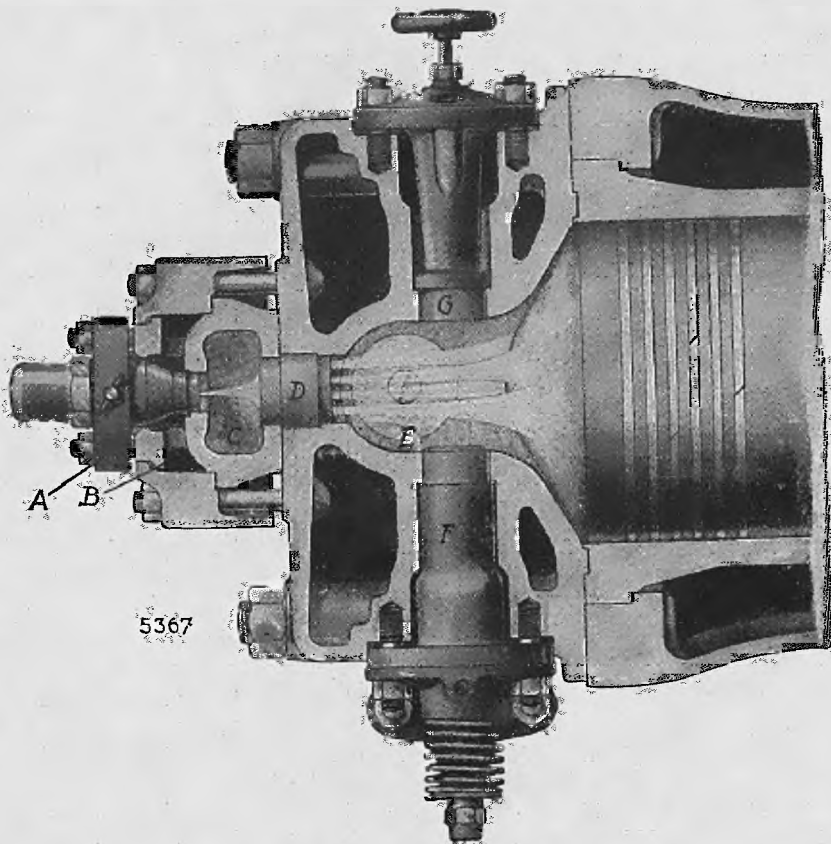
Schnitt durch den Zylinderkopf mit Vorkammer einer
